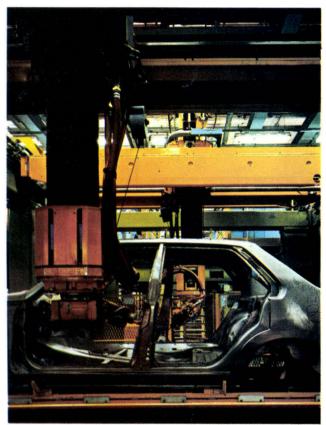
Photo B. - A l'usine de Flins, la soudure par points des Renault 18.
